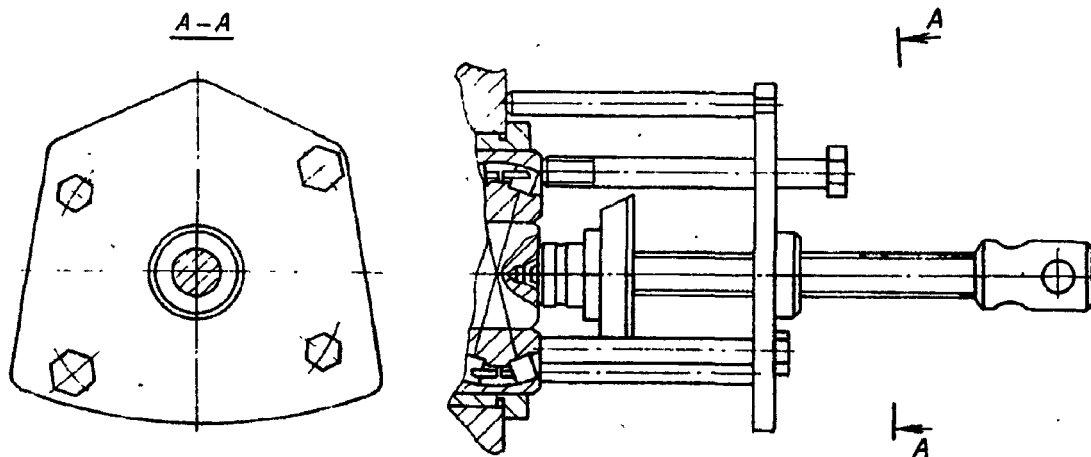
Снятие заднего подшипника ведущего вала со стаканом
